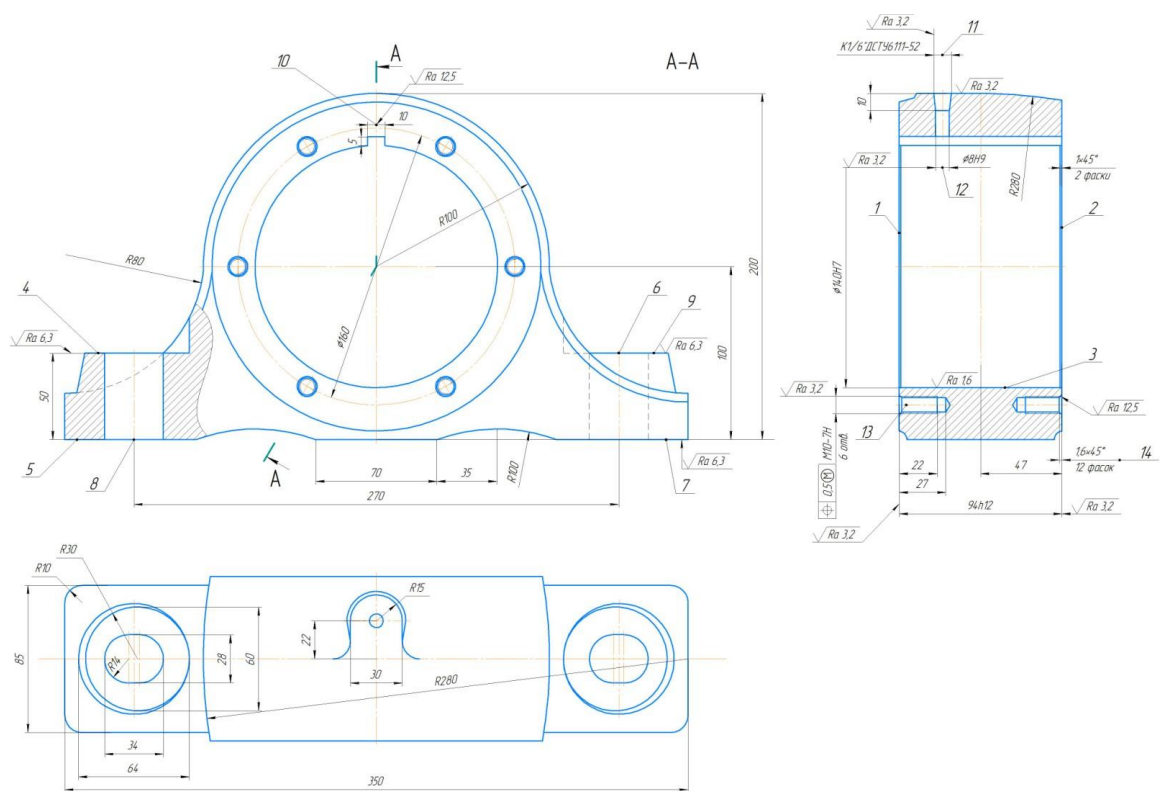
Нумерація поверхонь деталі «Корпус» привідного барабану
